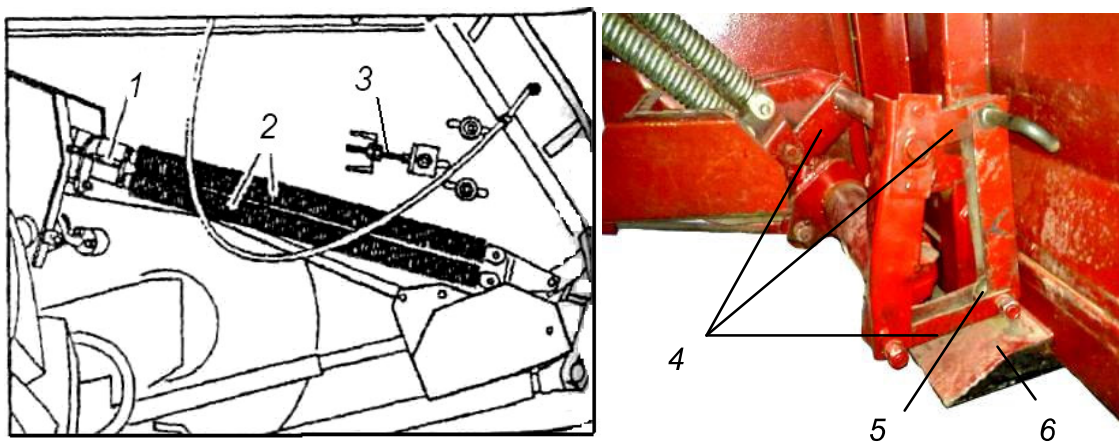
Механизм поперечного уравнивания: 1 – регулировочный винт; 2 – пружины; 3 – регулировочный винт натяжения транспортера наклонной камеры; 4 – система рычагов; 5 – ролик; 6 – кронштейн.
